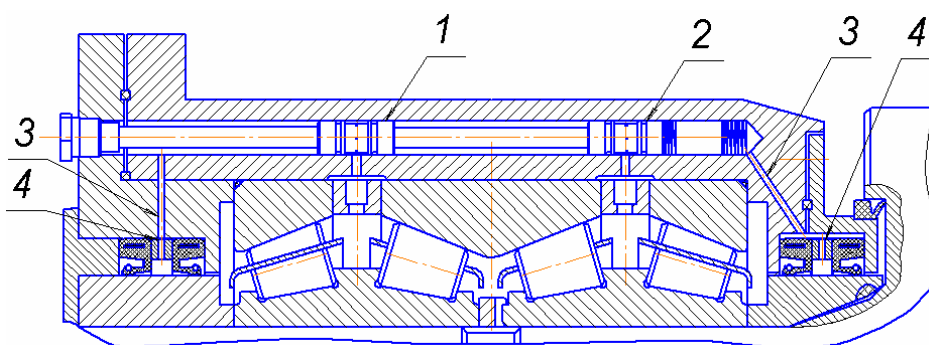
Установка делителей потока для смазывания подшипника и манжет
